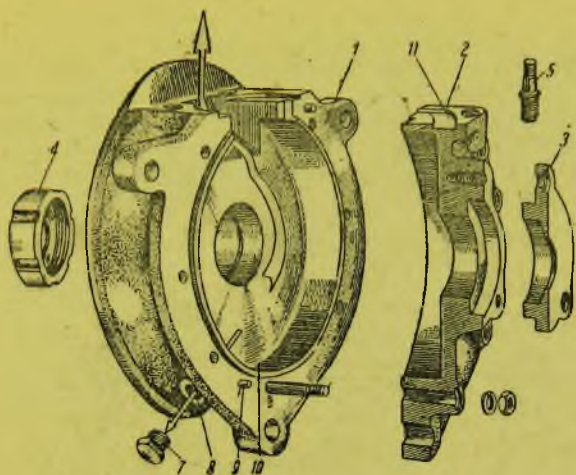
Картер двигателей ИЖ-7 и Л-300
